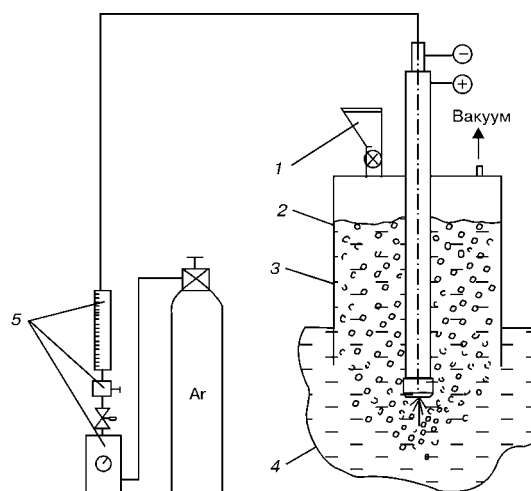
Схема процесса вакуумно-плазменной обработки расплава: 1 — дозатор реагентов; 2 — плазматрон; 3 — камера; 4 — расплав; 5 — система подвода газа
